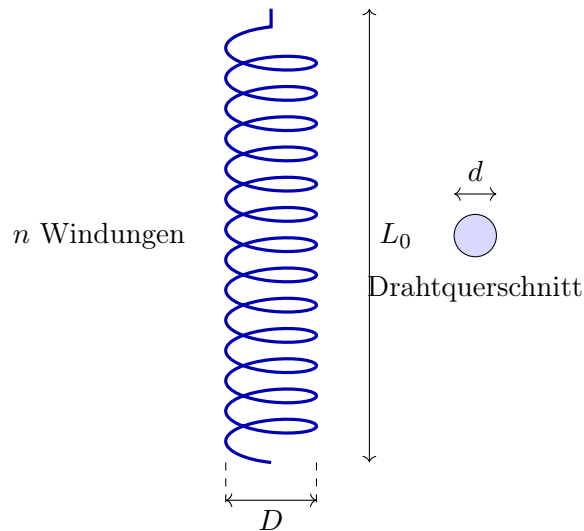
Geometrie der zylindrischen Schraubendruckfeder: Drahtdurchmesser  $d$ , mittlerer Windungsdurchmesser  $D$  (nicht der Außendurchmesser  $D_e$ !), ungespannte Länge  $L_0$ .
